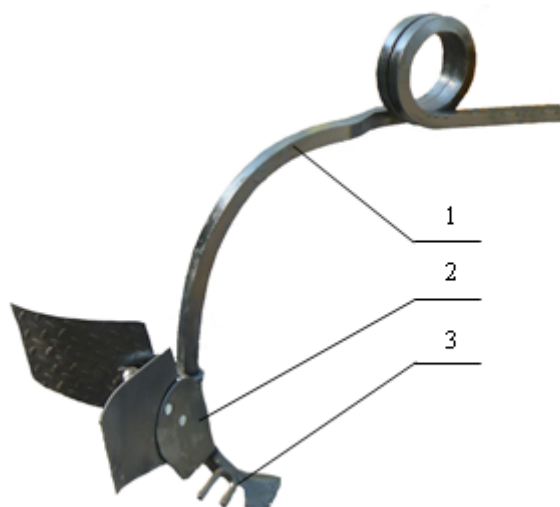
Корпус окучивающий на упругой стойке: 1 — стойка упругая; 2 — корпус окучивающий; 3 — лапа стрельчатая ярусная
